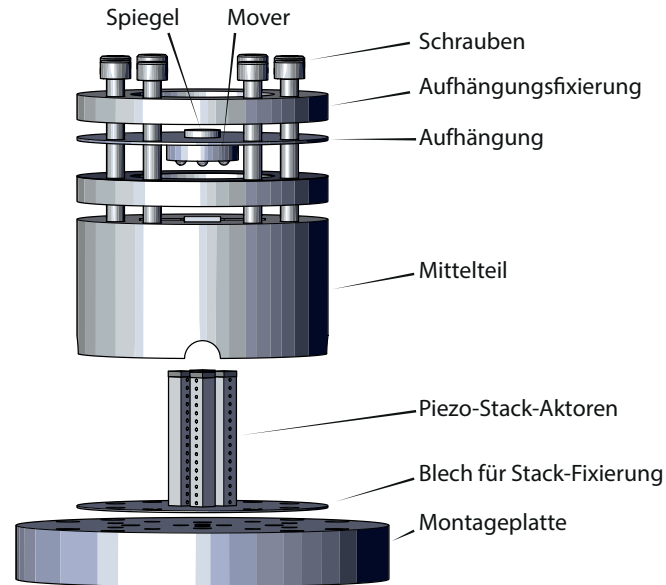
Komponenten des Kippspiegelsystems dargestellt in einer Explosionszeichnung.
